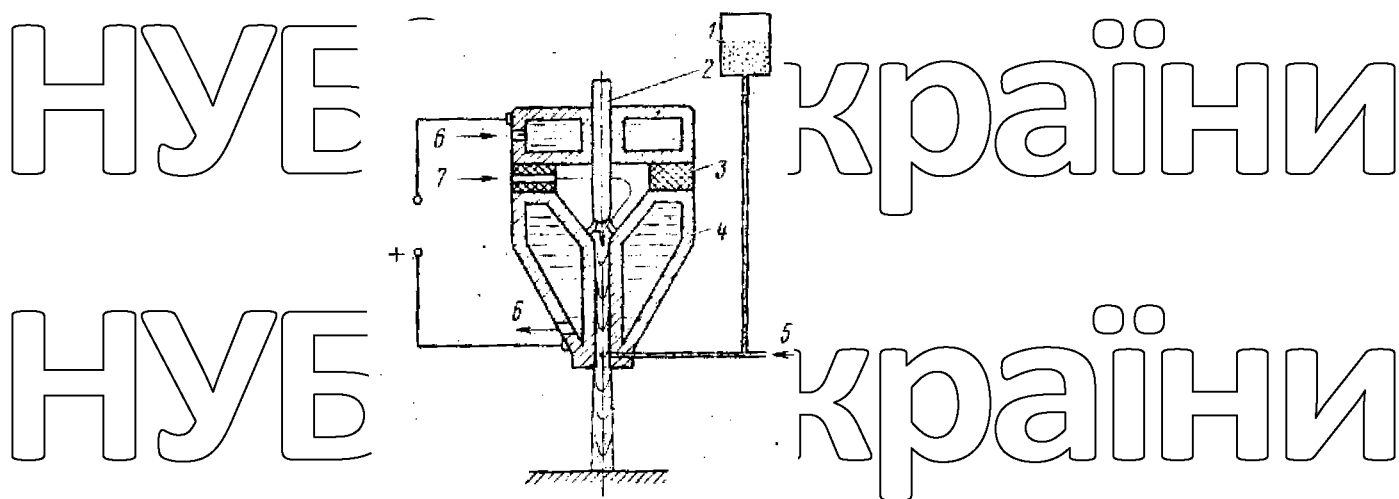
Схема пальника для плазмового напилення: 1 - порошок дозатор; 2 - катод; 3 - ізоляційна прокладка; 4 - анод (сопло); 5 - транспортуючий газ; 6 - охолодна вода; 7 - плазмоутворюючий газ
